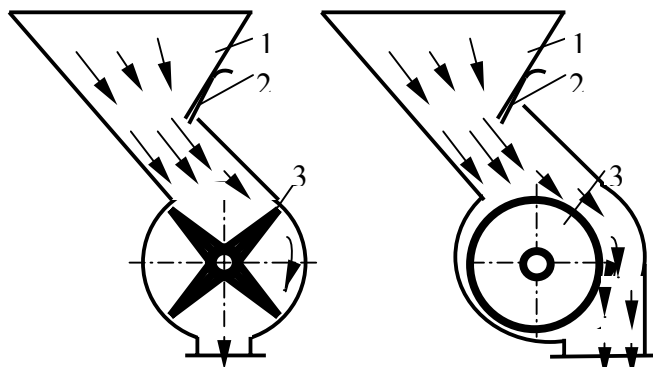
Схема барабанных питателей: 1- бункер; 2- шибберный затвор; 3- барабан; —> движение груза
